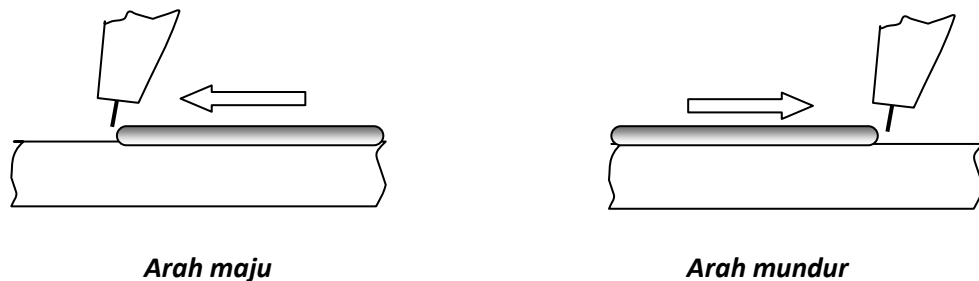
Posisi Pengelasan Pada Pipa
